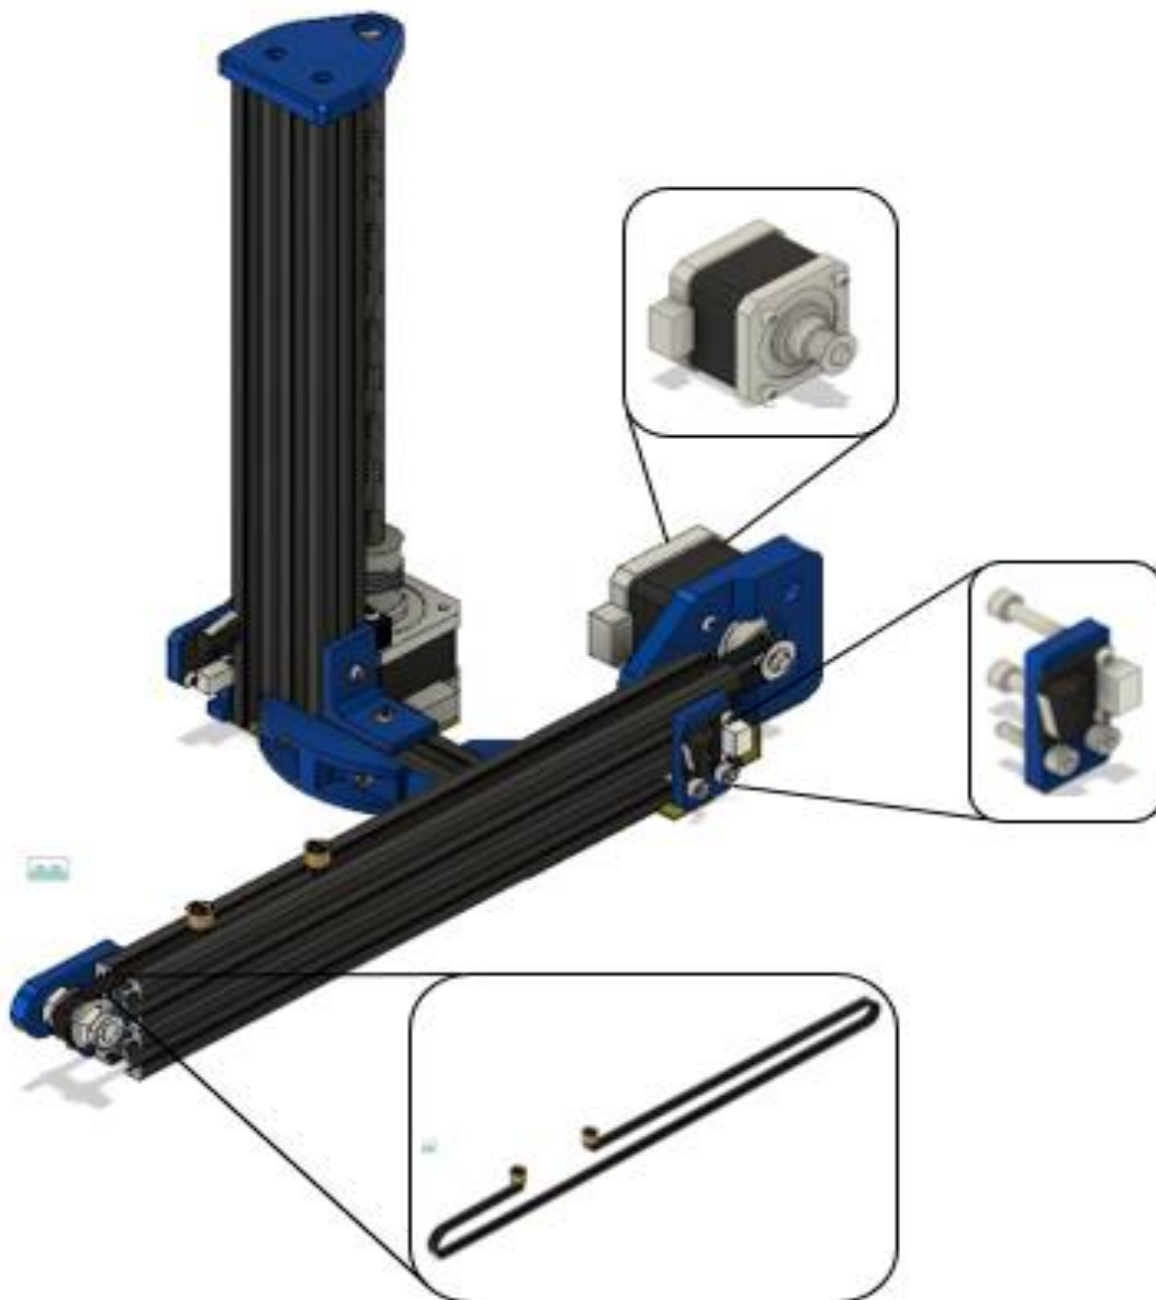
Ensamble del motor de eje Y, final de carrera y correa de la cama caliente
